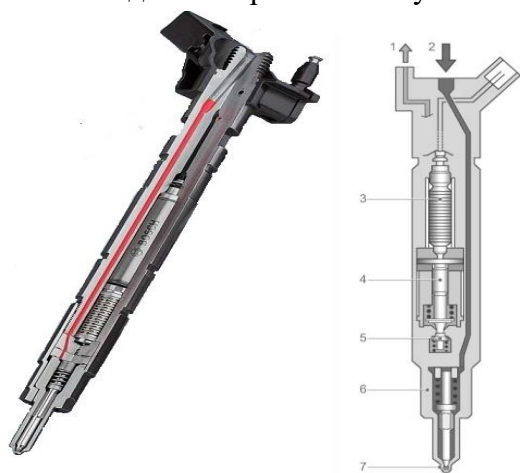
Конструкція форсунки з п'єзоелектричним приводом фірми Bosch: 1 - лінія зливу палива; 2 - лінія подачі палива; 3 - модуль п'єзоелектричного приводу; 4 - гідравлічний компенсатор; 5 - клапан керування; 6 - розпилювач; 7 – сопло
